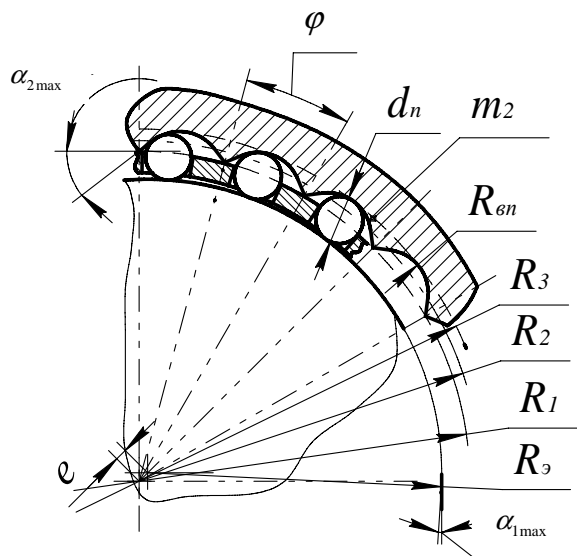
Профиль шарикового радиально-плунжерного редуктора
